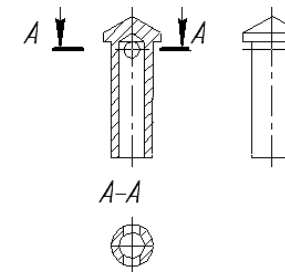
Зображення деталі «Клапан» на кресленику загального виду
